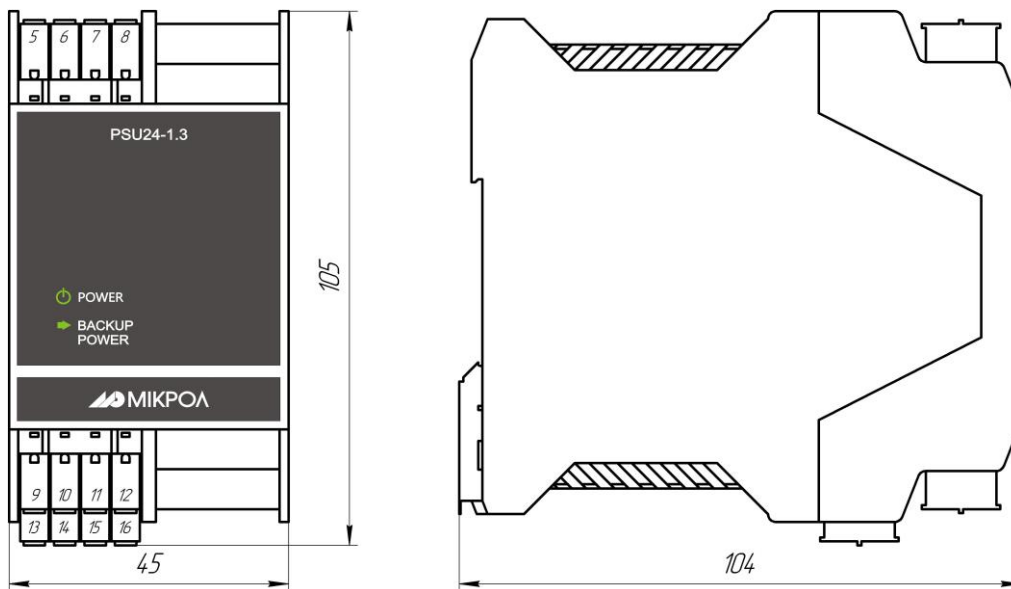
Внешний вид и габаритные размеры PSU24-1.3
